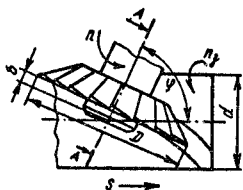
Схема фрезерования спиральной канавки угловой фрезой
